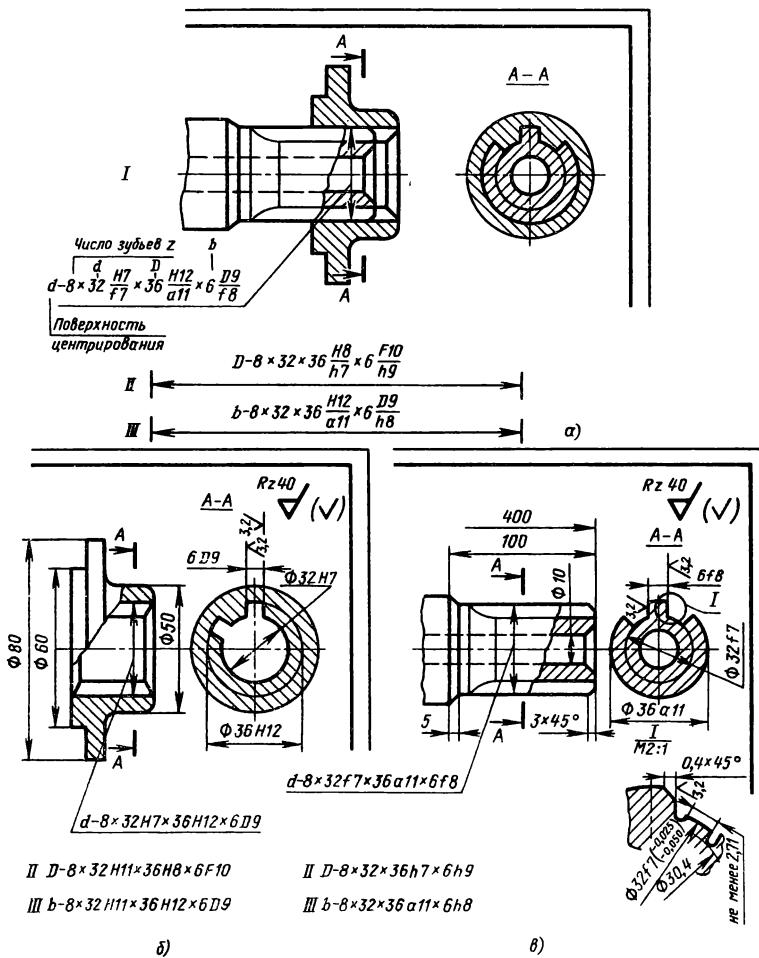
Обозначение допусков и посадок прямобочного шлицевого соединения на сборочном чертеже (а) и на рабочих чертежах деталей (б и в); варианты обозначения при центрировании:
